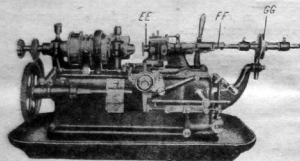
Подуавтомат Петерман для нарезки метчиков с приспособлением для фрезеровки резьбы.
